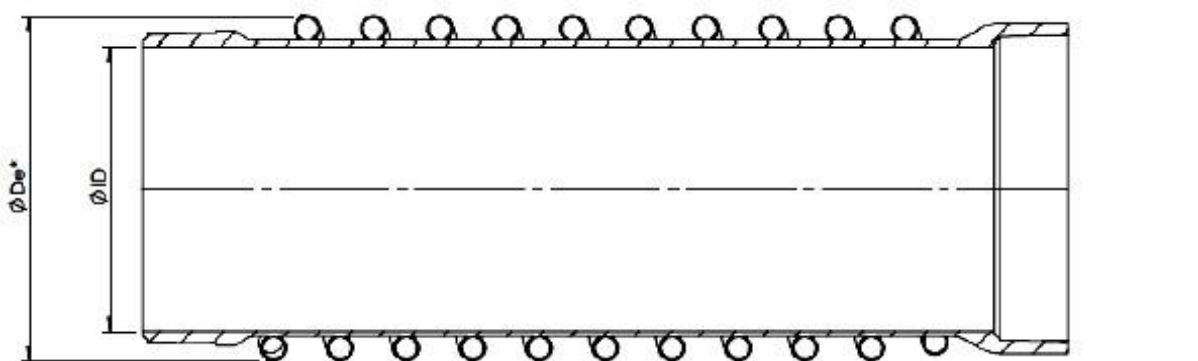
Общий вид и разрез трубы с профилем стенки «PR»
